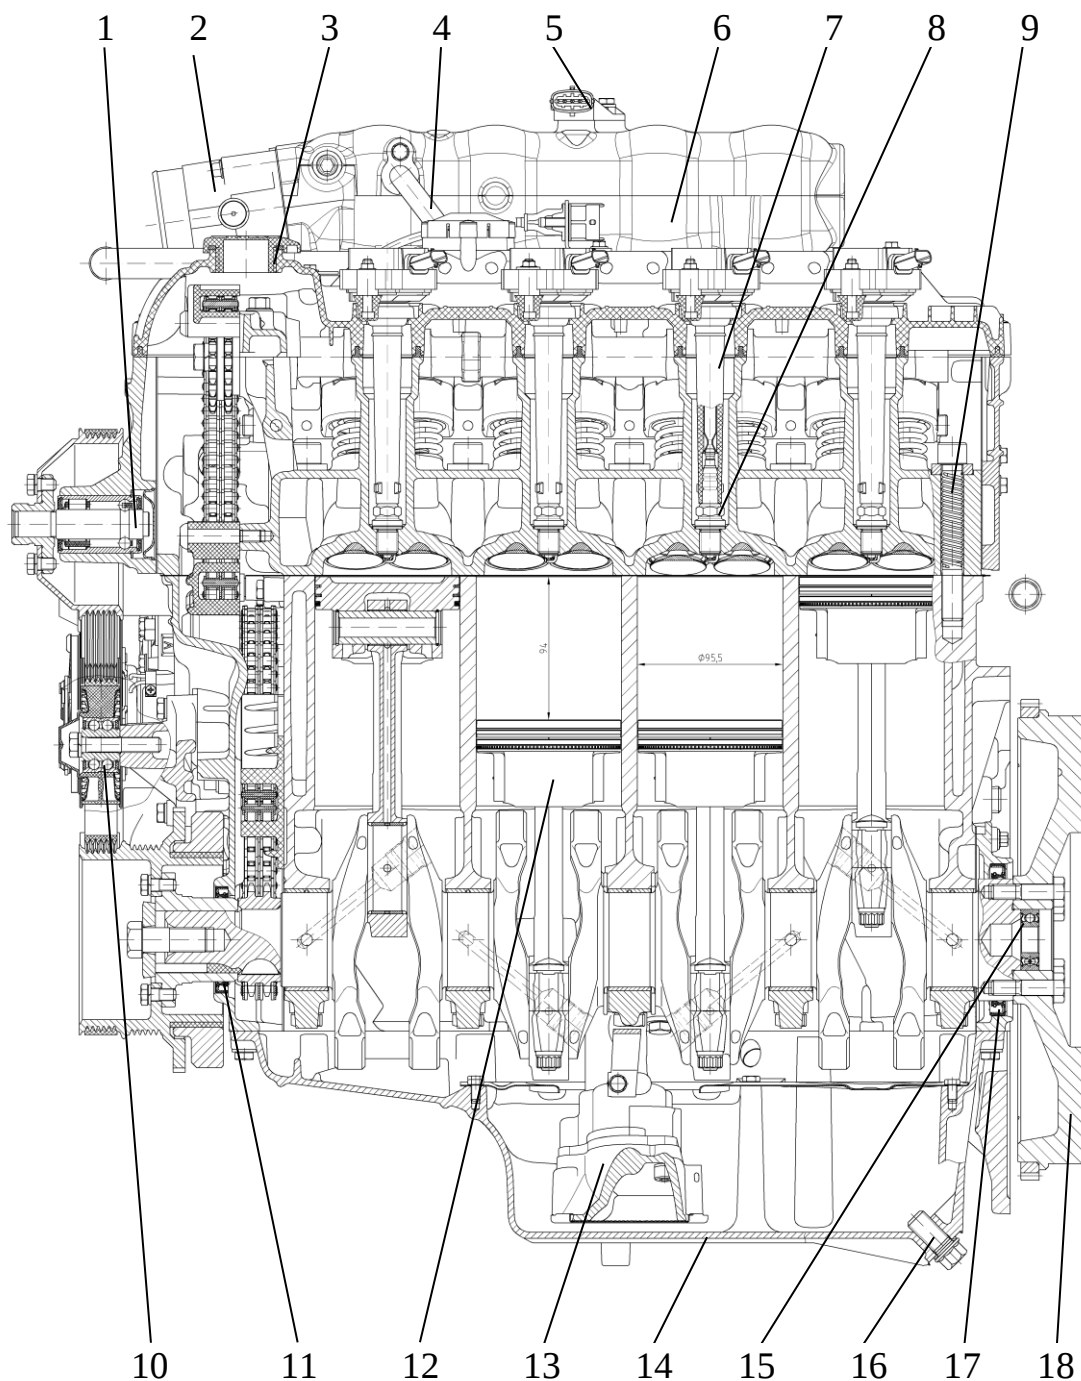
Продольный разрез двигателя с компрессором кондиционера:
